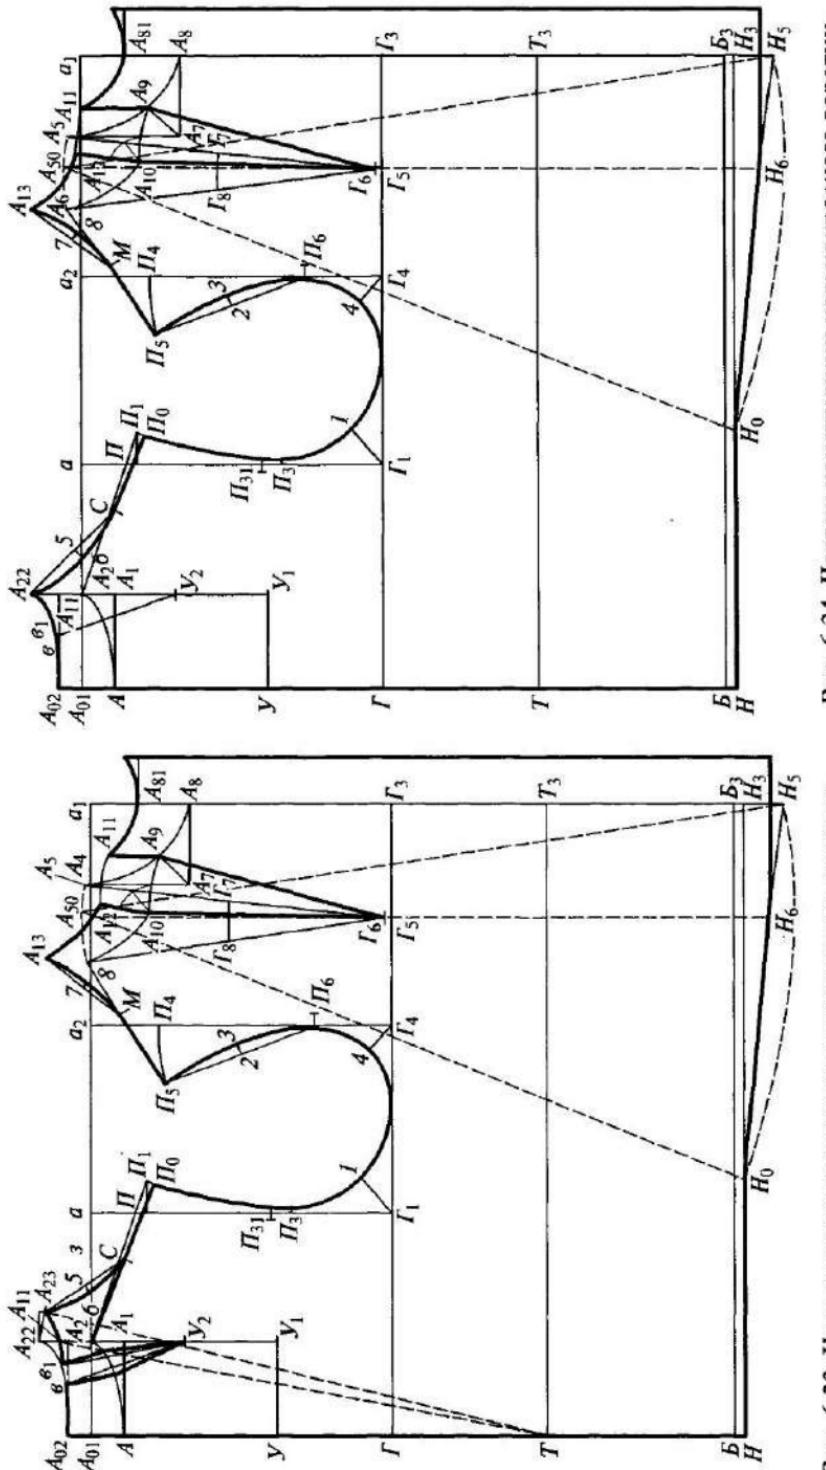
Чертеж конструкции цельнокроенного воротника (для фигуры с сутуловатой осанкой)
